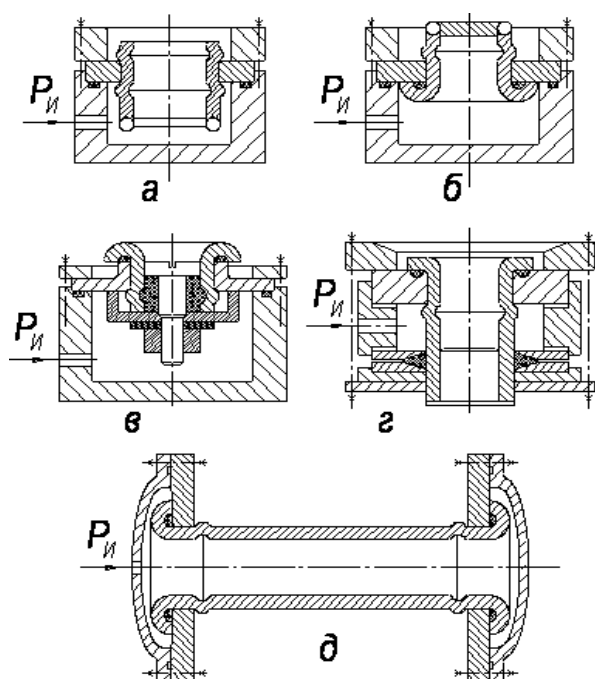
Приспособления и схемы для испытания образцов соединений труб с тонкой трубной решеткой: а - д – подача давления со стороны пучка труб и в трубное пространство.
